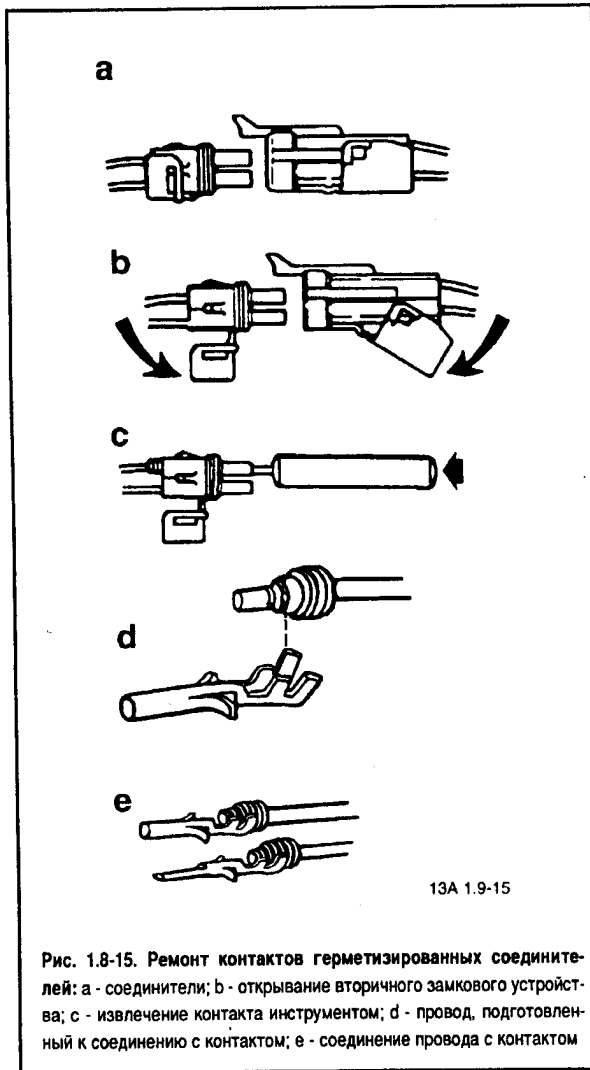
Ремонт контактов герметизированных соединителей: а - соединители; б - открывание вторичного замкового устройства; с - извлечение контакта инструментом; d - провод, подготовленный к соединению с контактом; е - соединение провода с контактом
